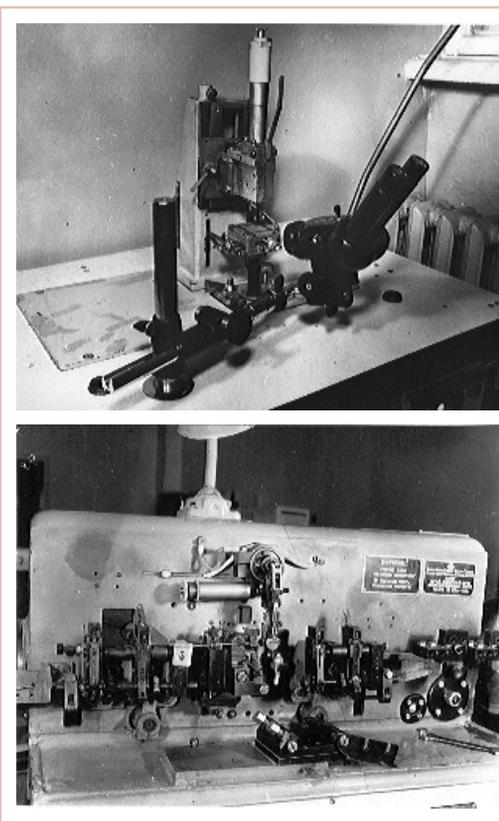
Примеры оборудования для ударной конденсаторной сварки, разработанного в ИЭС: а — универсальная сварочная головка установки К-543 для одиночной приварки проволоки к деталям различной конфигурации; б — сварочный узел автомата для сварки медных проволочных выводов диаметром 1,2 +0,8 мм
